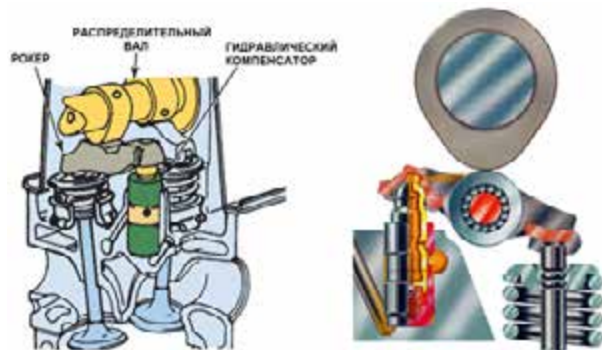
Использование гидравлического компенсатора вместо стойки пальцевого типа, являющегося опорой для качающегося рычага (рокера), позволяет избежать регулировки теплового зазора клапана; источник: *Pearson Education, Inc. u INA
